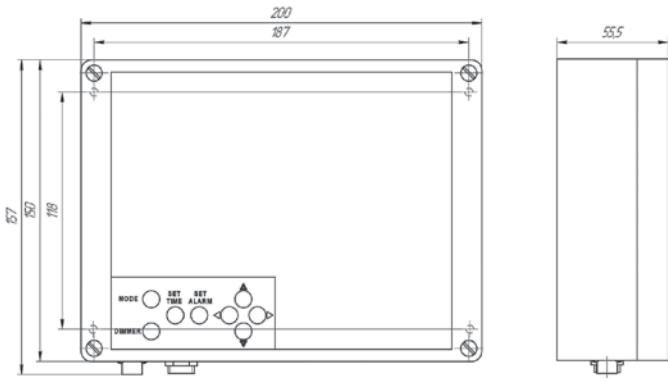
Габаритный чертеж ИПСС-00, ИПСС-01
